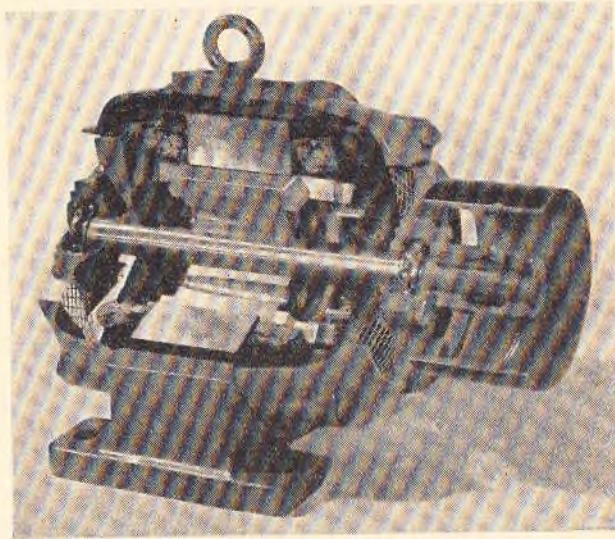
Drehstrommotor (geschnitten) mit Kurzschlußläufer
